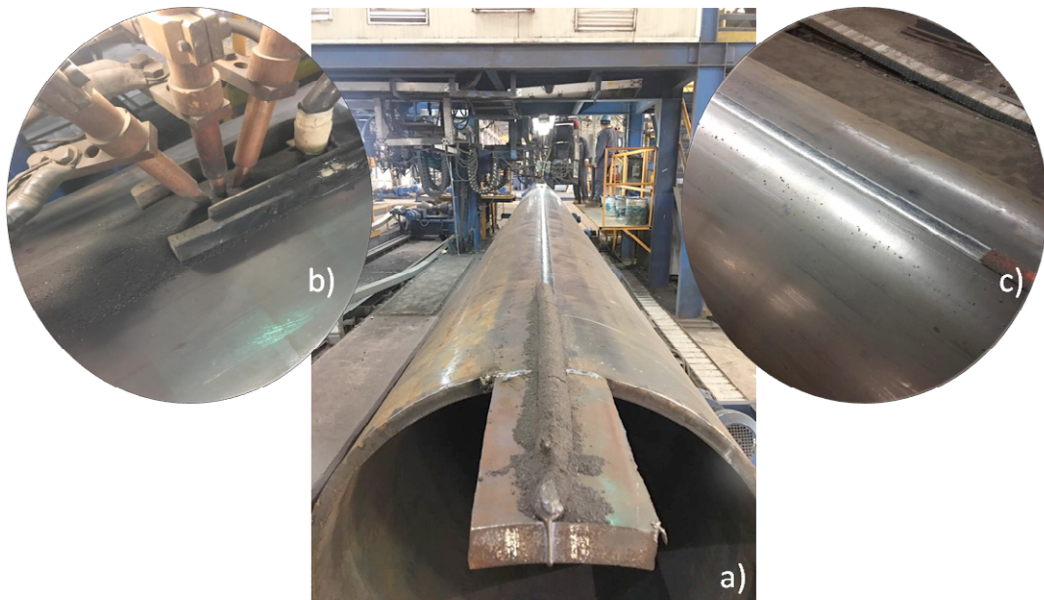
Fotografías que ilustran: a) salida de tubo API X52 (0.500 plg. de espesor y 40 plg. de diámetro) de celda de soldadura SAW mecanizada, b) acercamiento a los porta-alambres y dispensador de fundente, y c) cordón final. Fotografías cortesía de TUBACERO planta Pánuco
